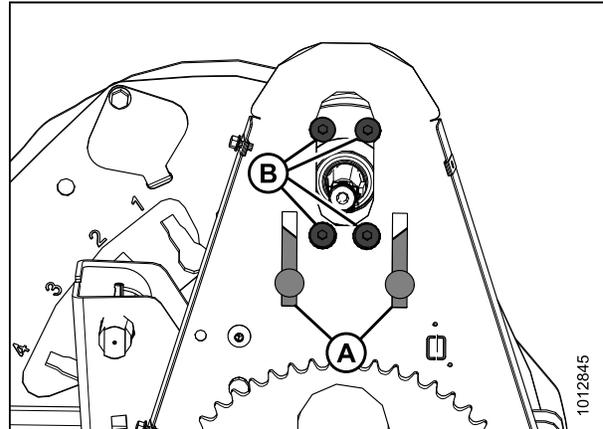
Монтажные отверстия мотора привода мотовила
